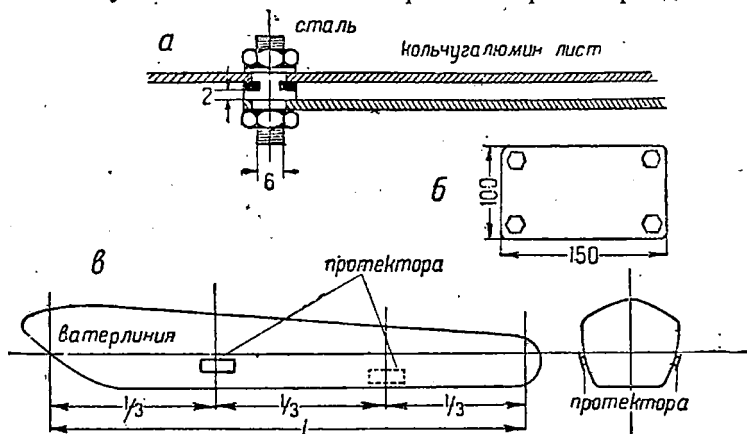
Установка протекторов на лодках и поплавках гидросамолетов.
